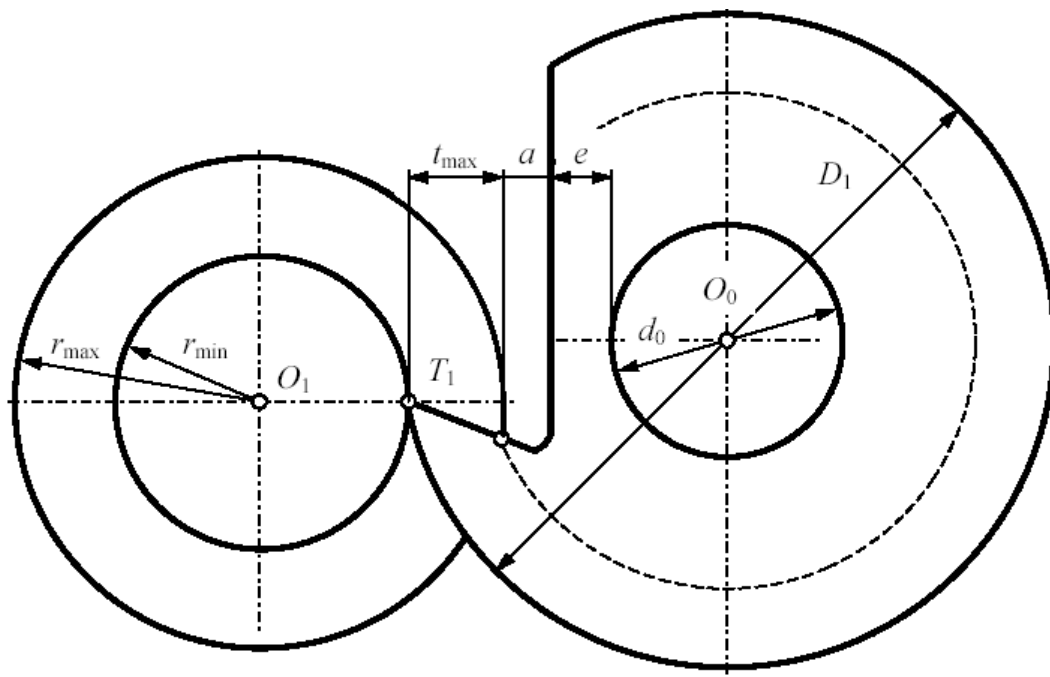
Фасонний круглий різець: розрахункова схема
